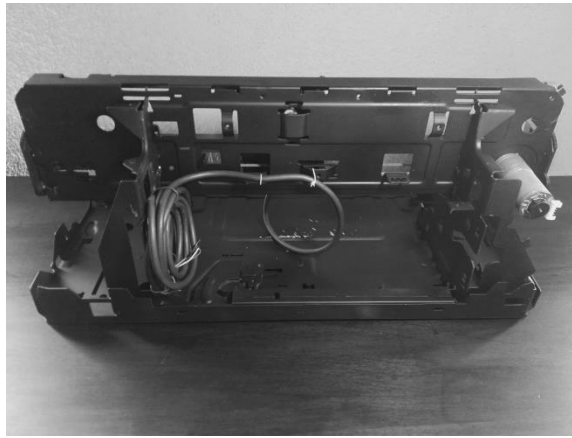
Vista posterior de marco de la impresora con codificador del péndulo y motor de engranajes de cc ensamblados.
